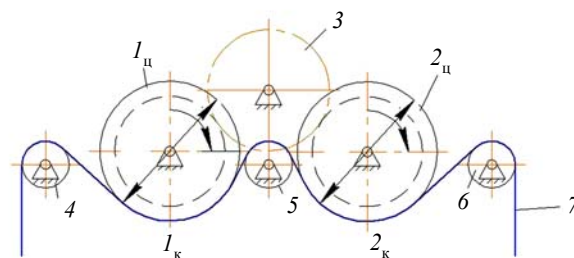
Фрагмент привода сушильных цилиндров: 1ц и 2ц – сушильные цилиндры; 1к и 2к – цилиндрические зубчатые колеса; 3 – паразитное колесо; 4, 5, 6 – сетковедущие валы; 7 – сетка
